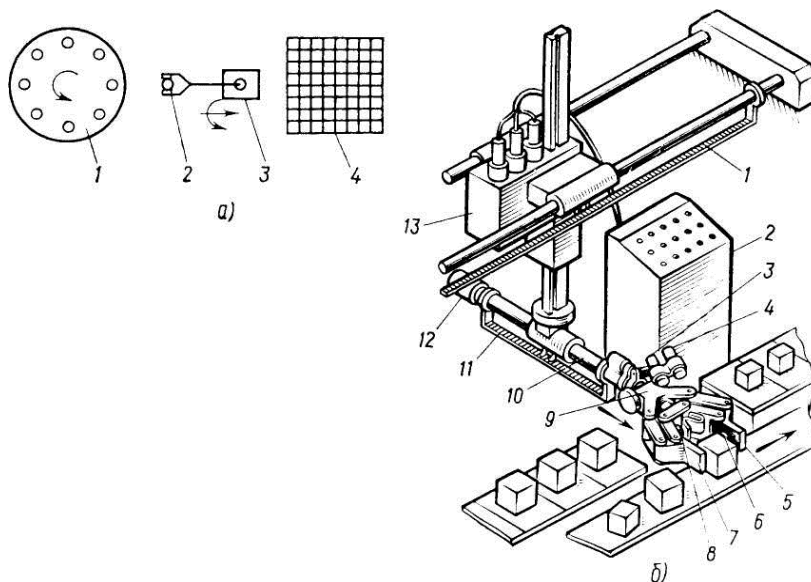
Робот-рассортировщик: а) схематическое изображение; б) общий вид
